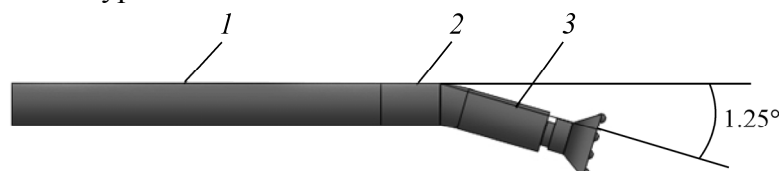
Буровой рабочий орган на основе забойного двигателя: 1 — забойный двигатель; 2 — переходник; 3 — привод в сборе
